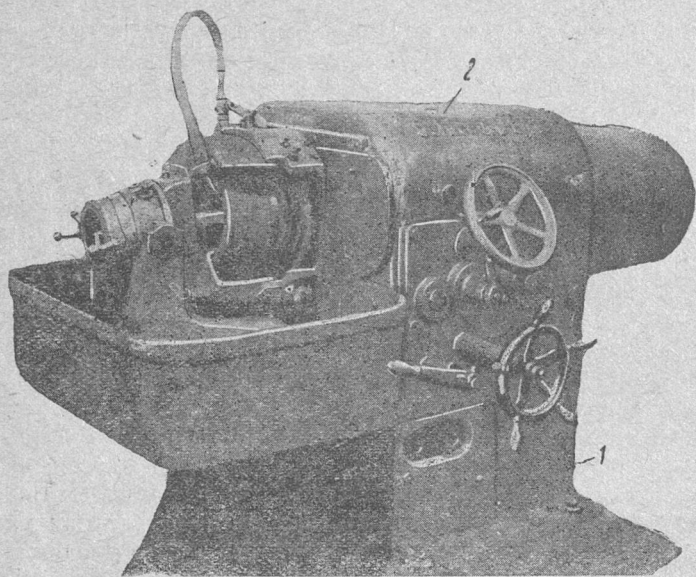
Общий вид станка Шисс-Дефриз для заточки резцов.
